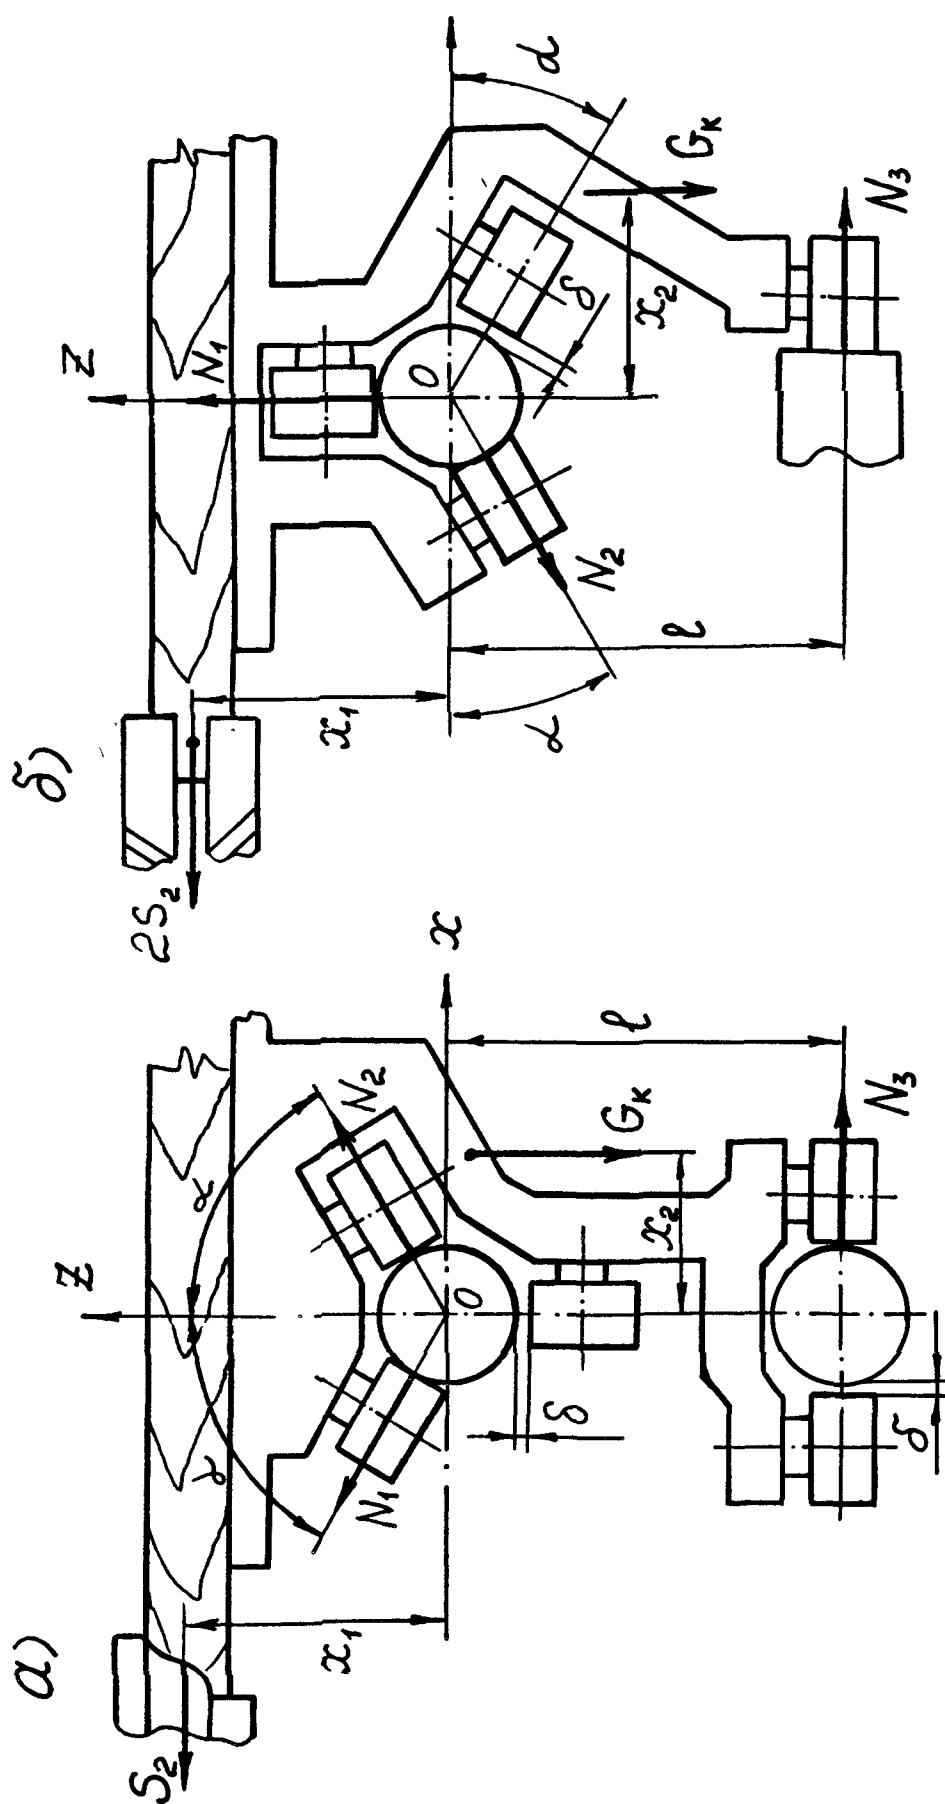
Расчетные схемы для определения реакций в опорах: а) фрезерного станка с шипорезной кареткой; б) шипорезного одностороннего станка
